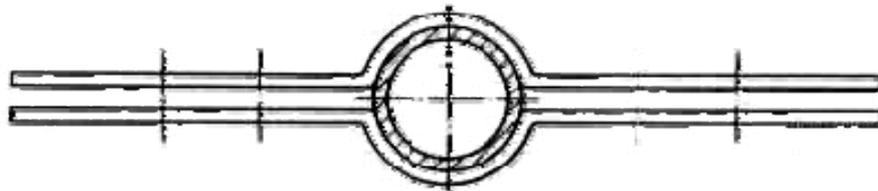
Braçadeiras de transporte e montagem para tubos de coluna
